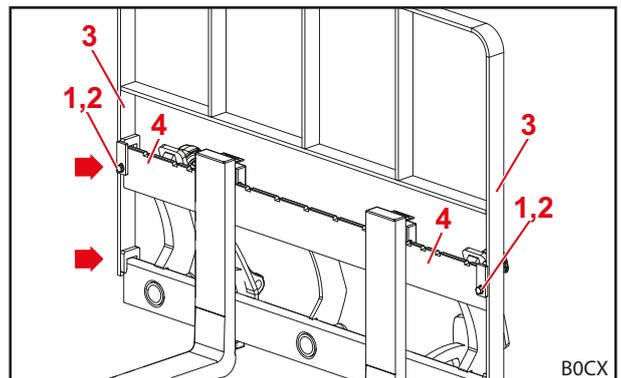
Rejilla de retención montada en la horquilla portapalets
